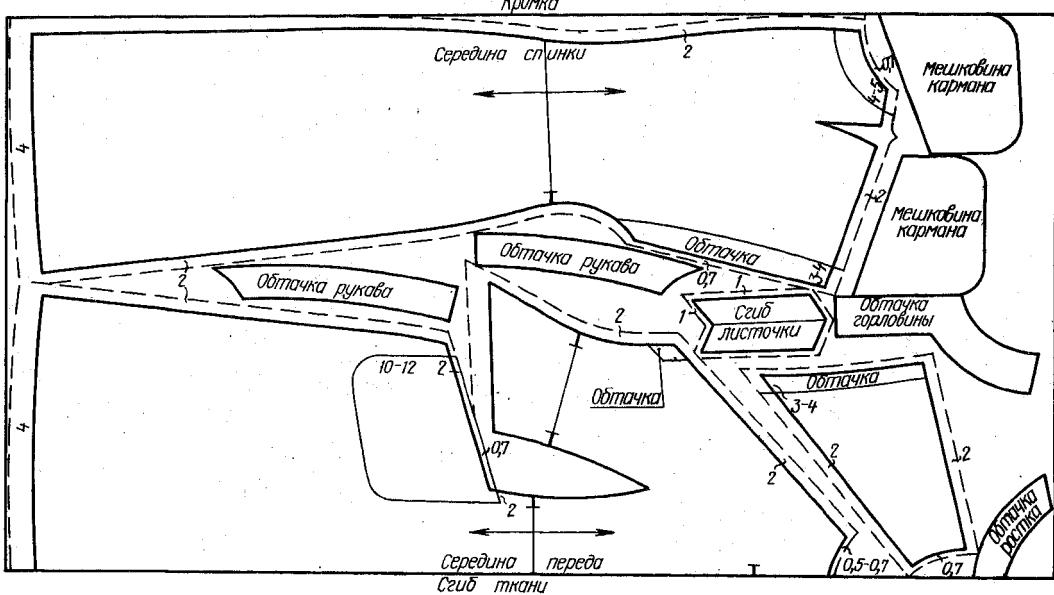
Раскладка выкроек на ткани и раскрой платья-сарафана на кокетке
